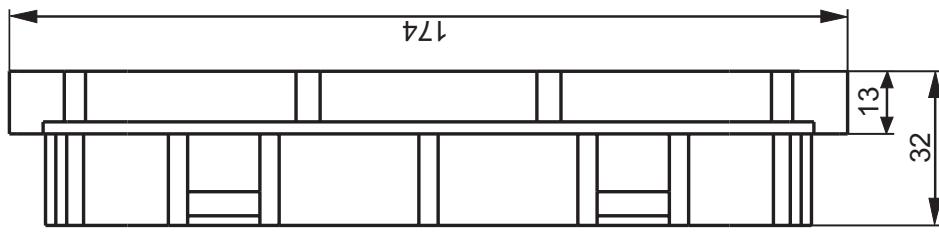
Габаритные и установочные размеры корпуса монтажного
